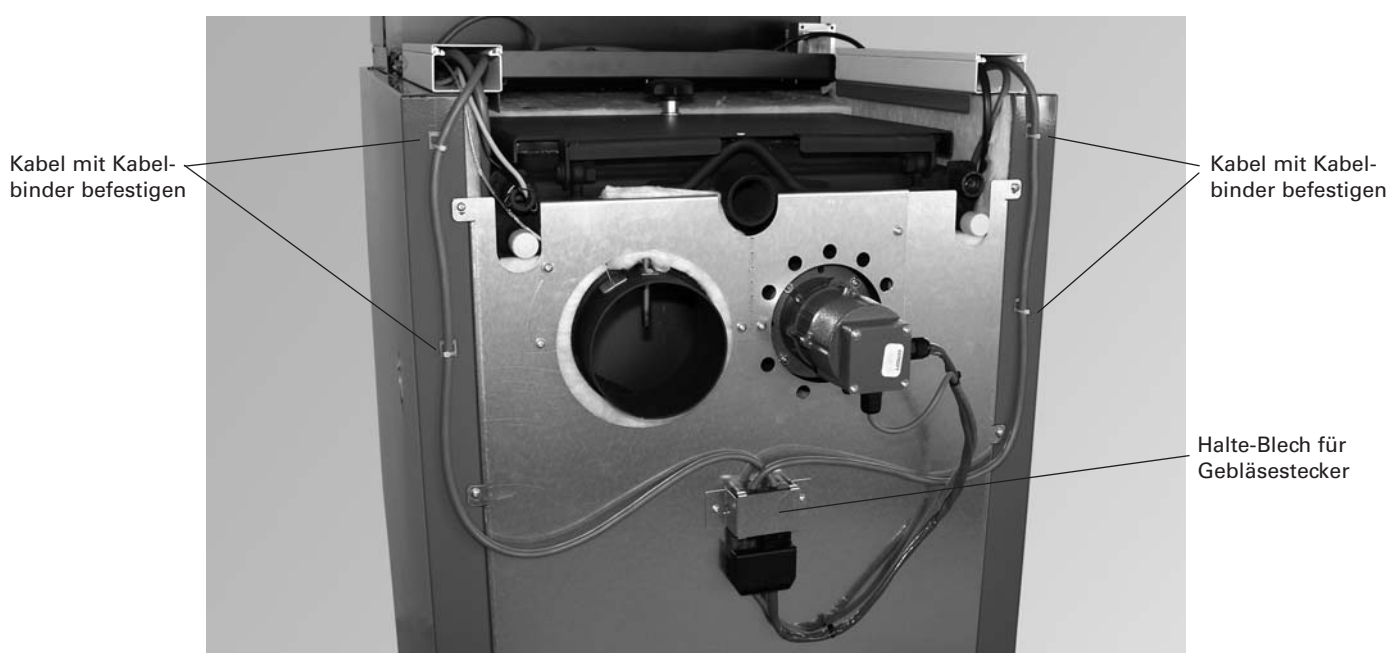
Rückwand montieren, Halte-Blech mit Stecker vom Gebläse an Rückwand oben anschrauben, Kabel mit Kabelbinder seitlich befestigen
